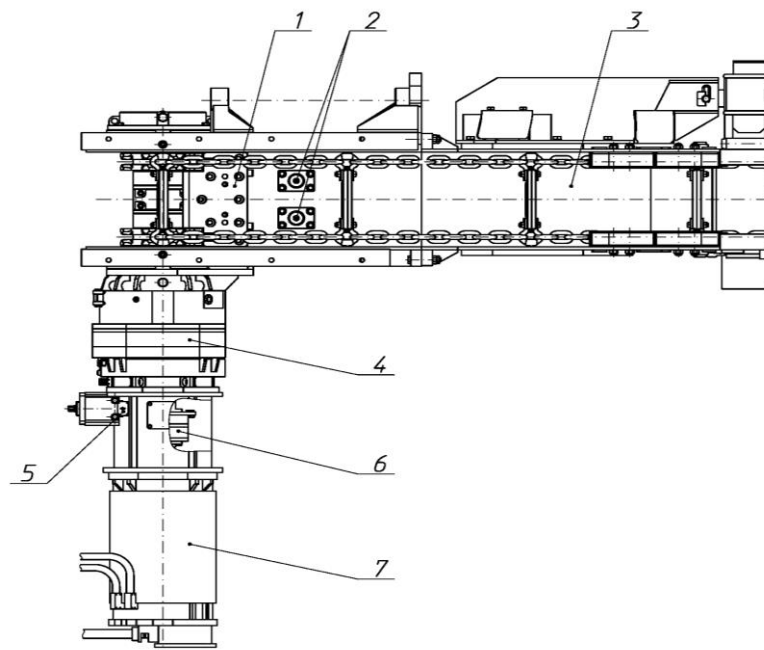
Приводной блок конвейера СПД 26 с поперечным расположением двигателя:
